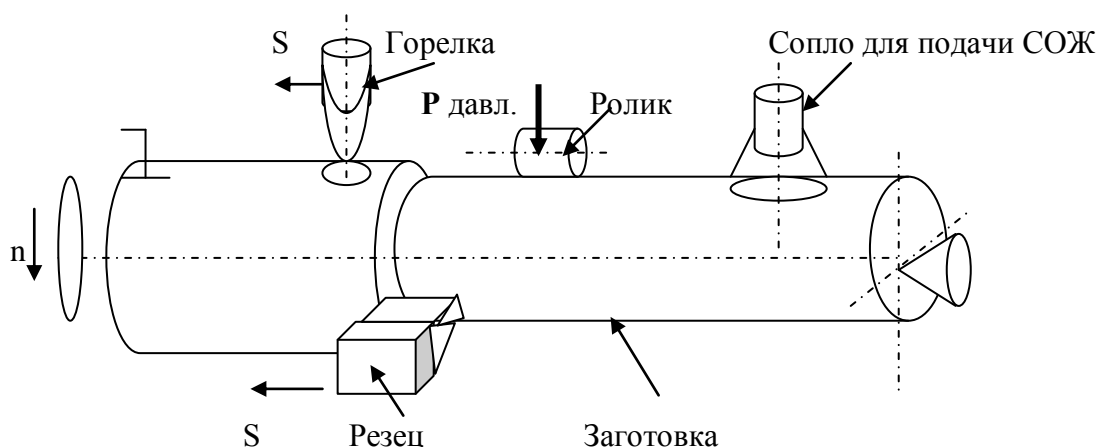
Схема термодинамической обработки нагретой поверхности детали
